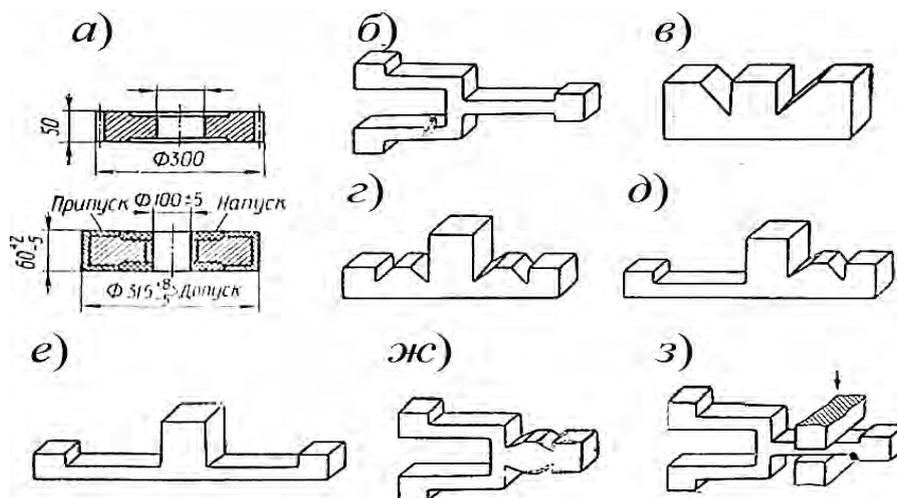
Чертеж поковки (а) и схемы процессаковки рычага с вилкой (б–з)
